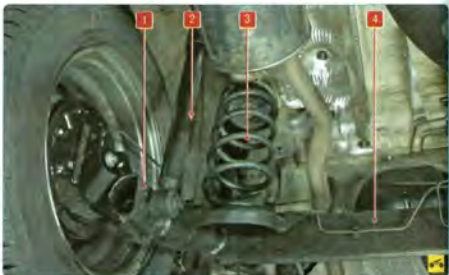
Задняя подвеска автомобиля 2WD: 1 – продольный рычаг; 2 – амортизатор; 3 – пружина; 4 – балка
